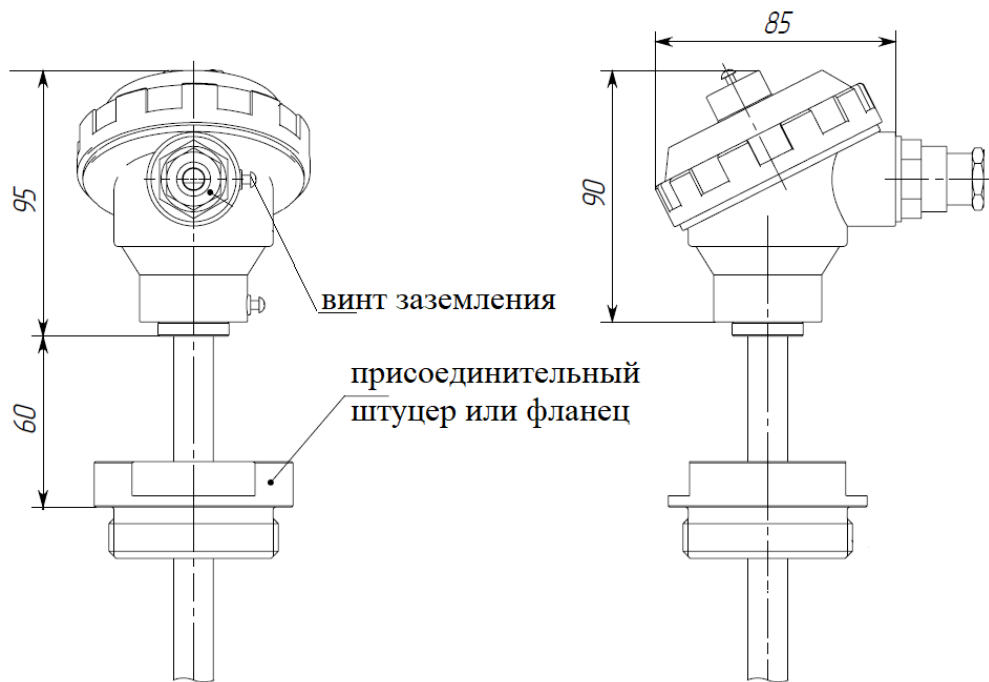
Габаритные размеры сигнализатора с корпусом А80.
